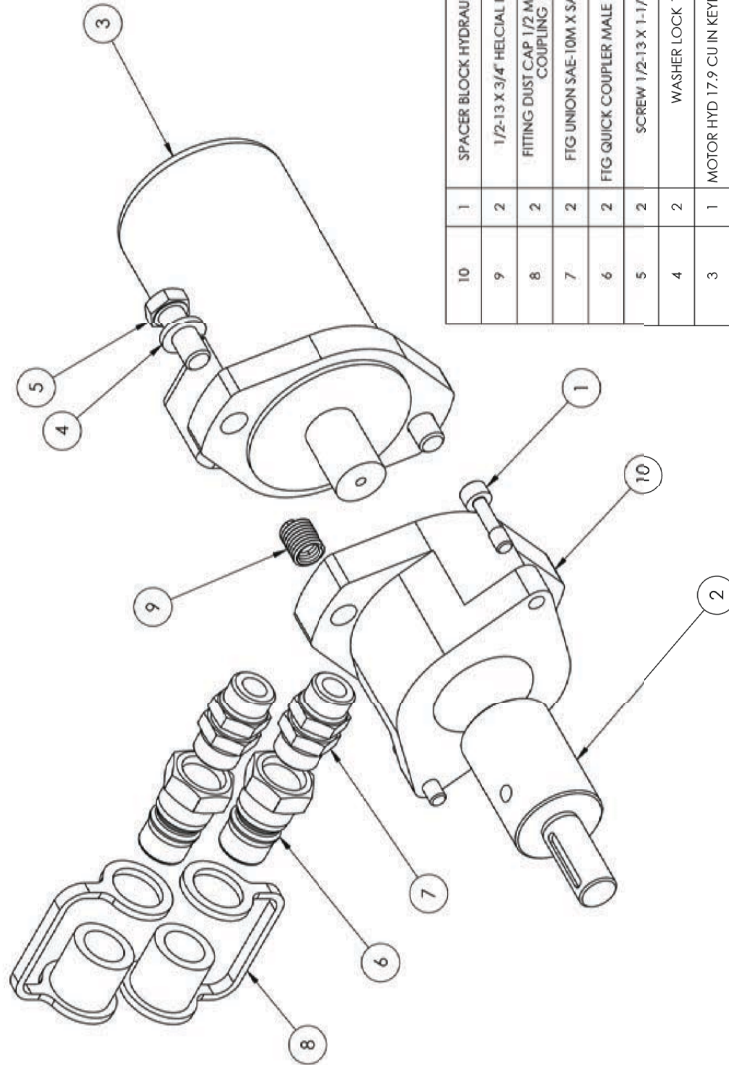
CONJUNTO DEL PIE DE EXTENSIÓN (N/P 87164)
